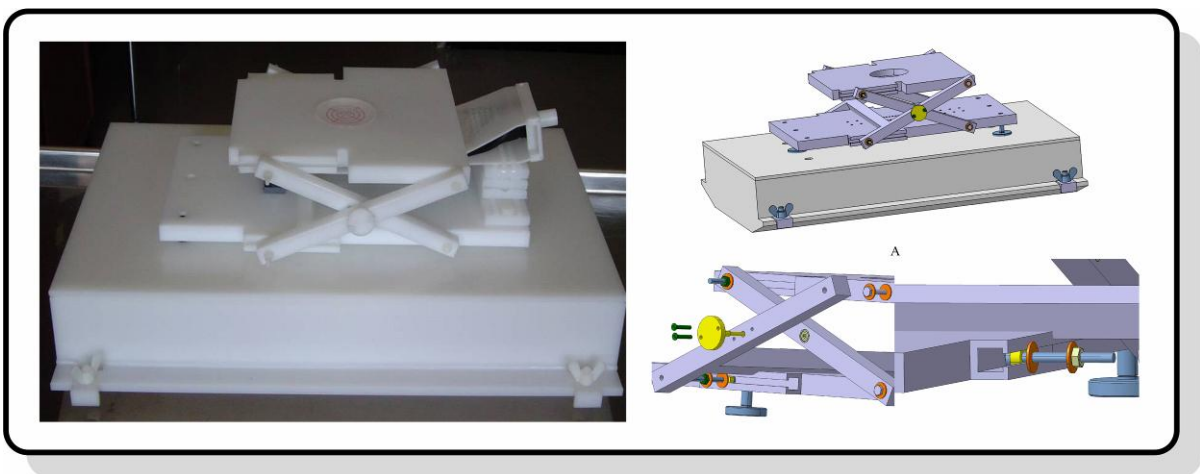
Plate-forme mobile. Vue générale du dessin en Conception Assistée par Ordinateur et photo du dispositif assemblé
